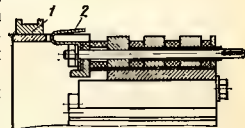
Короткозамыкающее приспособление с пружинными контактами
